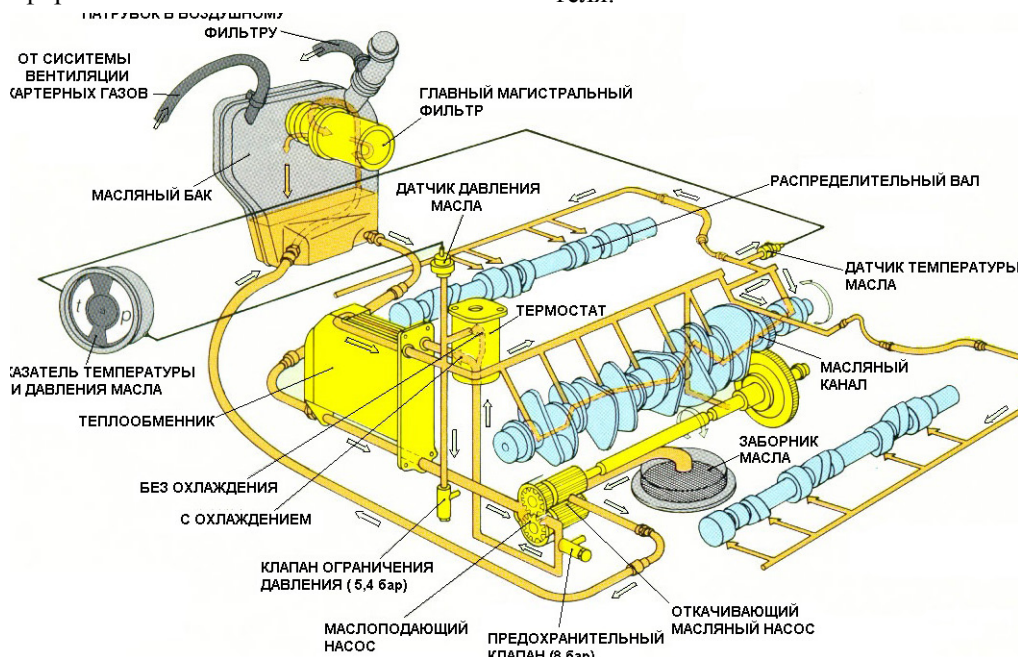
Система смазки с приводом масляного насоса от коленчатого вала, и «сухим» картером; источник: Kraftfahrzeugtechnik (TAK)
